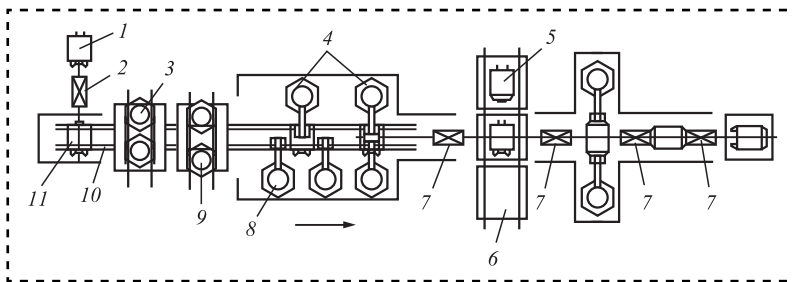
Роботизированный пост линии сборки-сварки кузовов легковых автомобилей:
